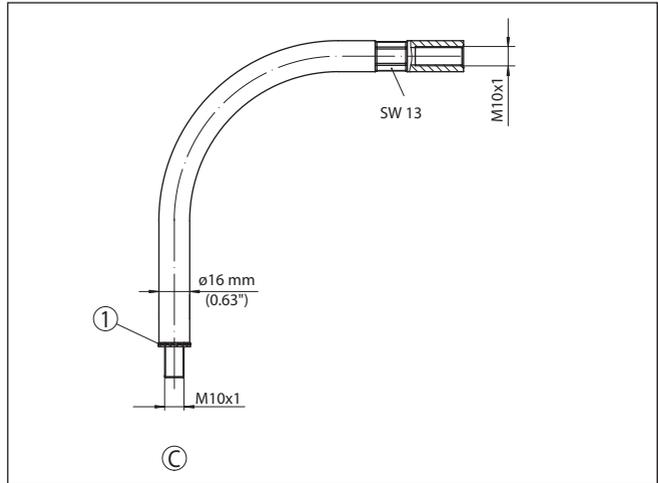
Componentes de varilla y cable con \varnothing 16 mm (0.63 in)
